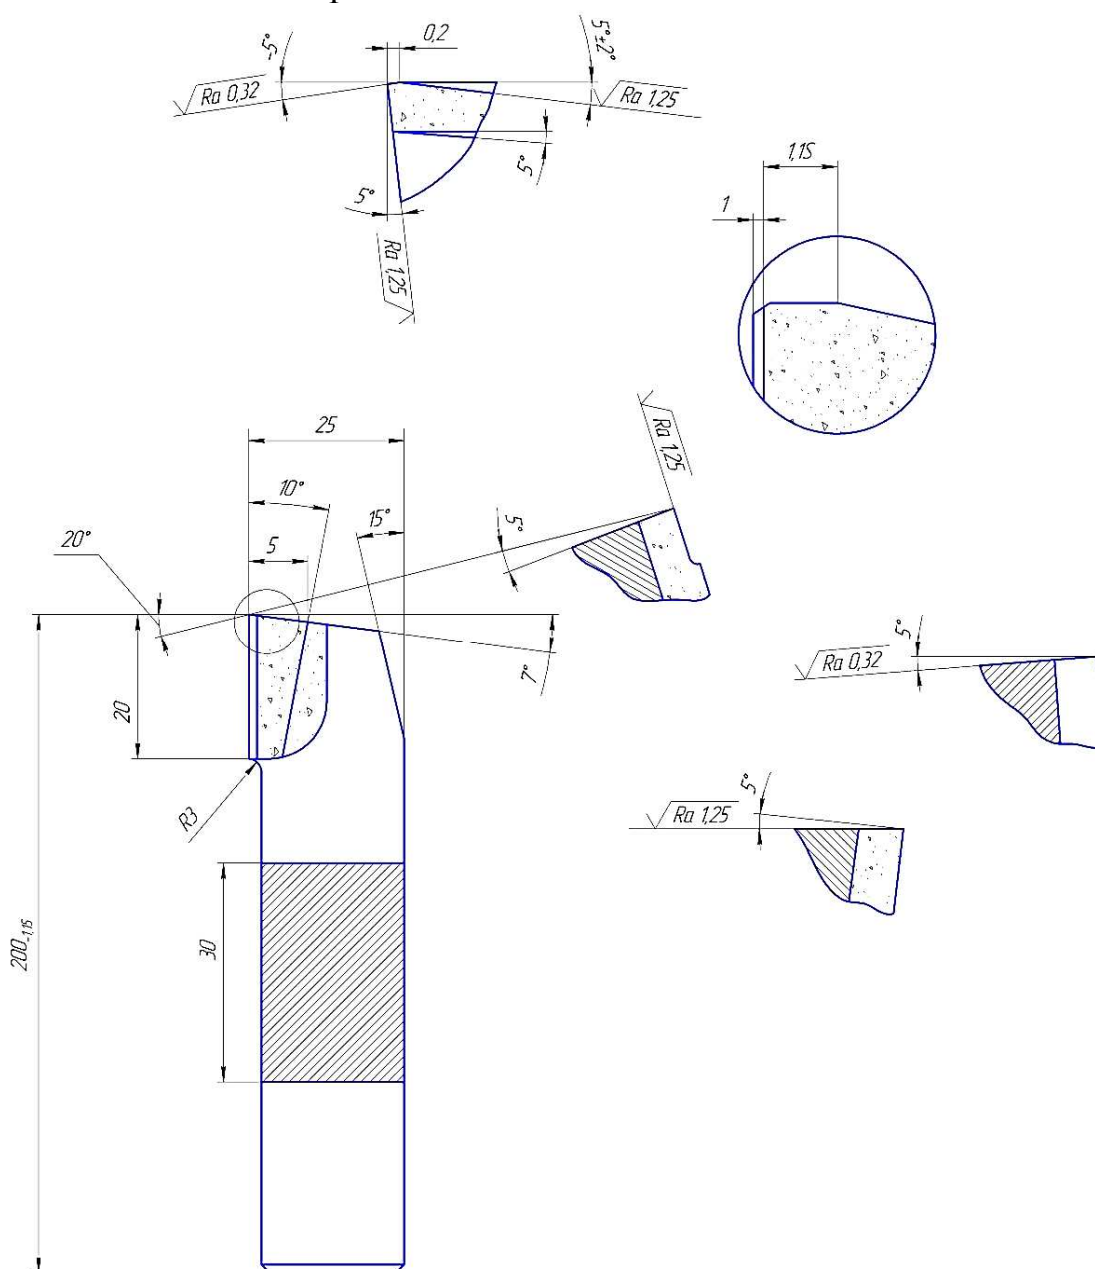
Резец В.А. Колесова для точения ступенчатых валков: пластинка твердого сплава Т15К6
